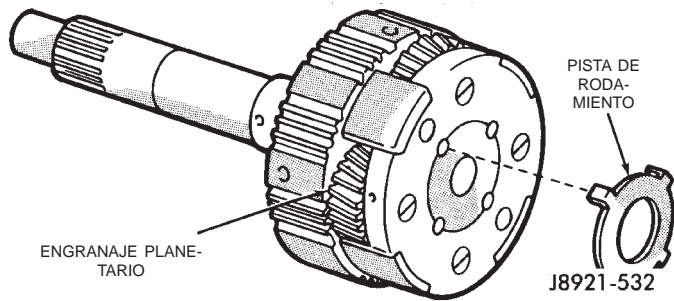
Desmontaje de la pista de rodamiento del engranaje planetario
